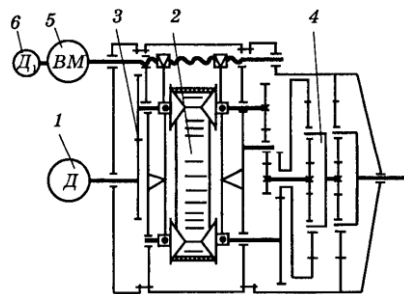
Привод з варіатором і планетарним редуктором: 1 – асинхронний електродвигун; 2 – ланцюговий варіатор; 3 – зубчаста пара; 4 – планетарний редуктор; 5 – виконавчий механізм; 6 – спеціальний електродвигун
